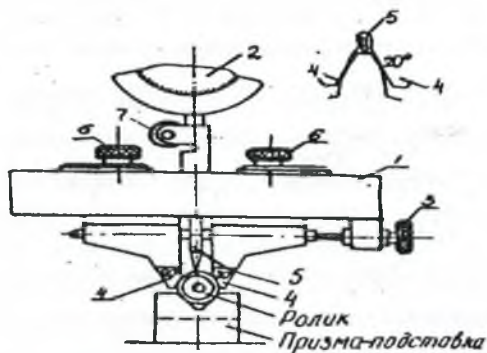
Настройка тангенциального зубомера и измерение: 1 – корпус зубомера; 2 – индикатор часового типа; 3 – винт для перемещения измерительных губок зубомера; 4 – измерительные губки зубомера; 5 – измерительный стержень индикатора; 6 – гайки для закрепления измерительных губок; 7 – винт для закрепления индикатора; $\alpha_d = 20^\circ$ – угол зацепления.
